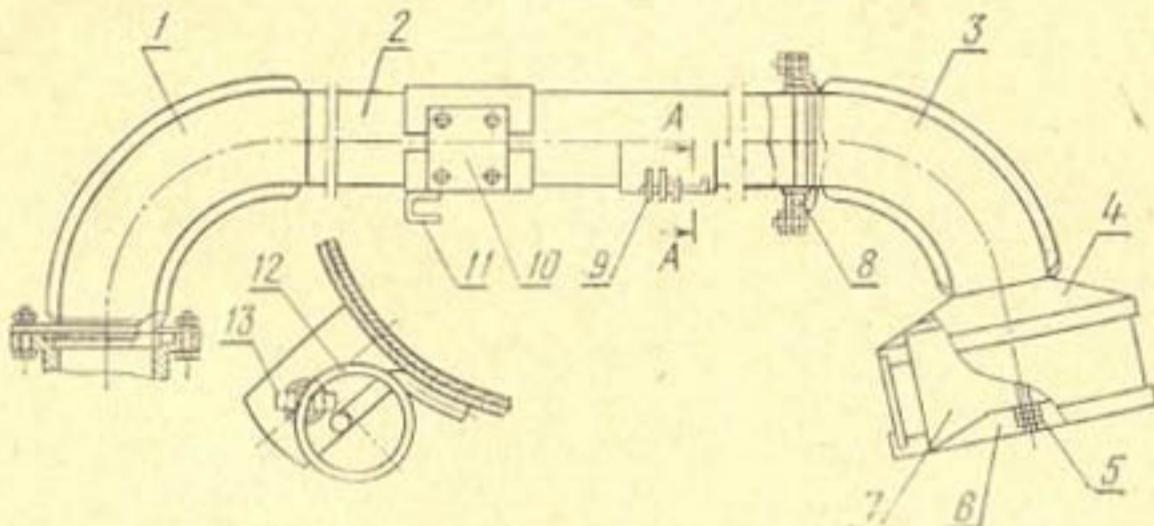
Всасывающий трубопровод дождевателя ДДН-70:
